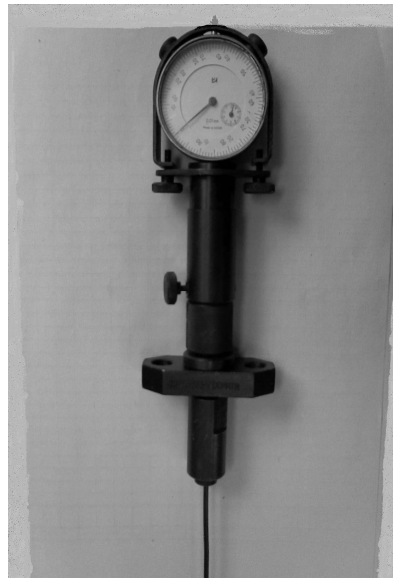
Прибор КИ-13933-ГОСНИТИ
